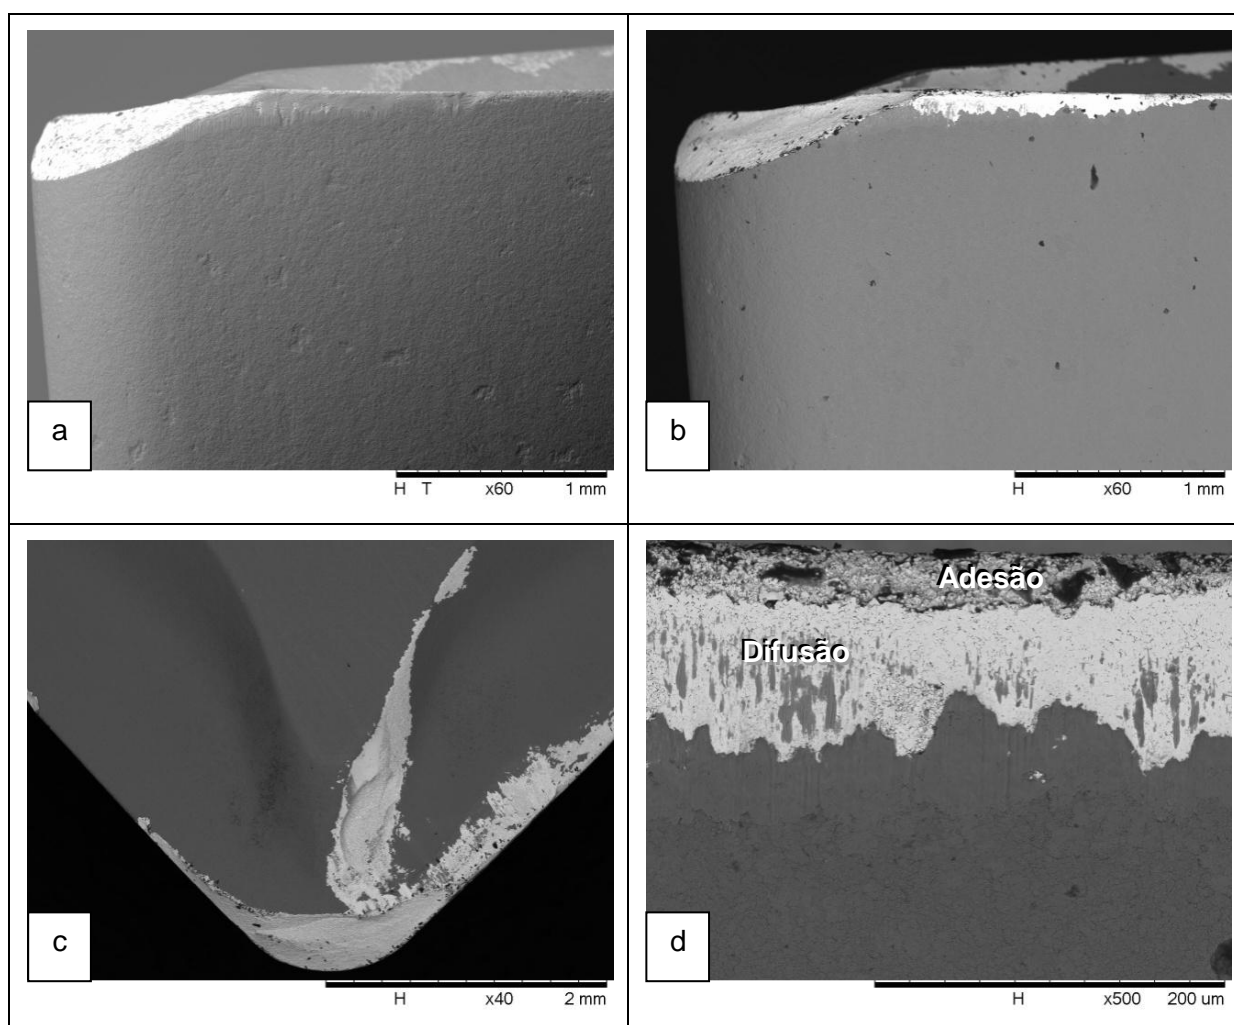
Superfície de folga e de saída da ferramenta utilizada na usinagem do material B para o ensaio de vida 03 ($v_c = 100,00$ m/min, $f = 0,20$ mm/volta e $a_p = 2,00$ mm).a)
